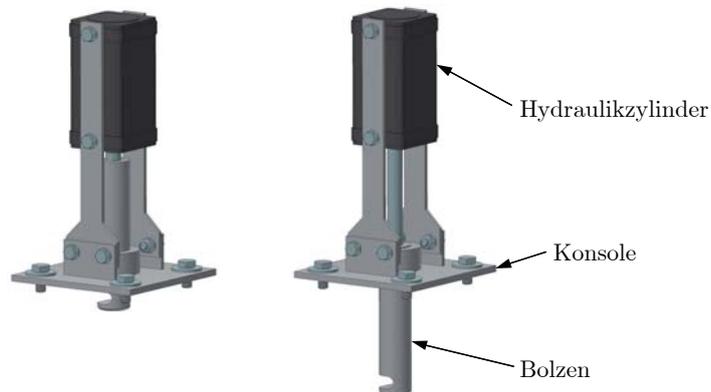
Hydraulikzylinder mit Bolzen zum Betätigen des Hebelmechanismus
